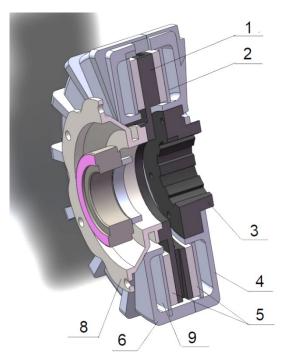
Доработанный дисковый тормозной механизм с пневматическим приводом и кольцевыми тормозными колодками: 1 – тормозной диск; 2 – тормозная колодка; 3 – крепление оси; 4 – внутренняя часть корпуса; 5 – кольцевая фрикционная накладка; 6 – внешняя часть корпуса; 7 – воздушная камера; 8 – переходник ступицы
